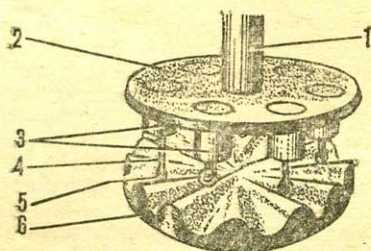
Схема двигателя без коленвала: 1 — ось, 2 — диск с цилиндрами, 3 — цилиндры, 4 — шток поршня, 5 — ролик, 6 — опорный гофрированный диск.
